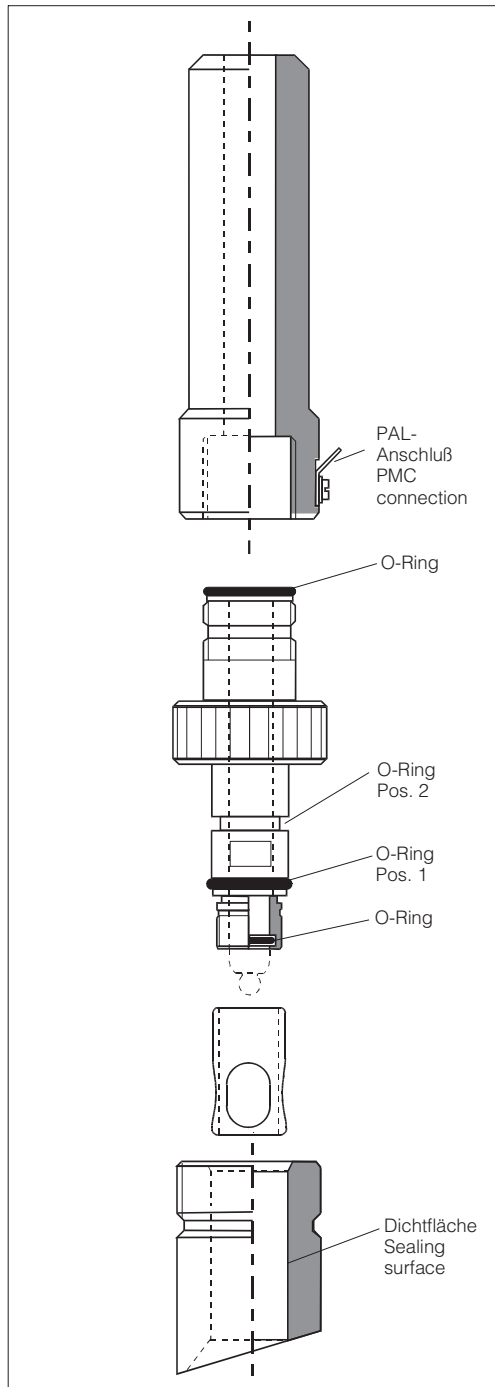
O-Ring-Montage Proffit CPA 440 Adapter DN 25
